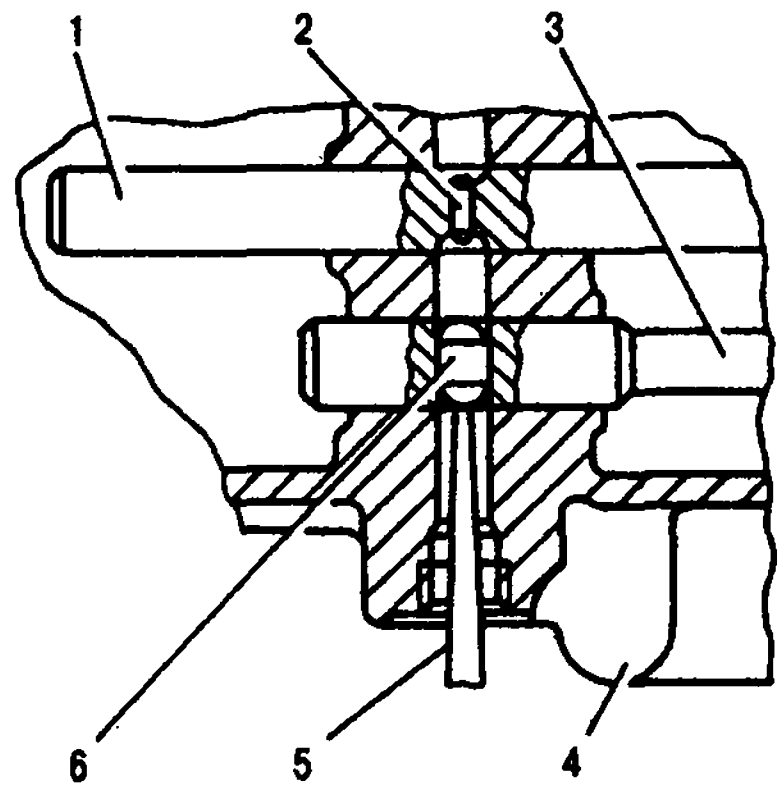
Установка стопорного плунжера: 1 - стопорный палец; 2 - шток; 3 - оправка; 4 - задний картера; 5 - бородок; 6 - стопорный плунжер
